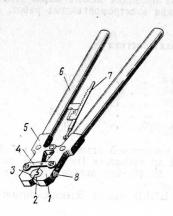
1 — головка; 2 — матрица; 3 — пуансон; 4 — рычаг подвижный; 5 — устройство блокирующее; 6 — рычаг неподвижный
